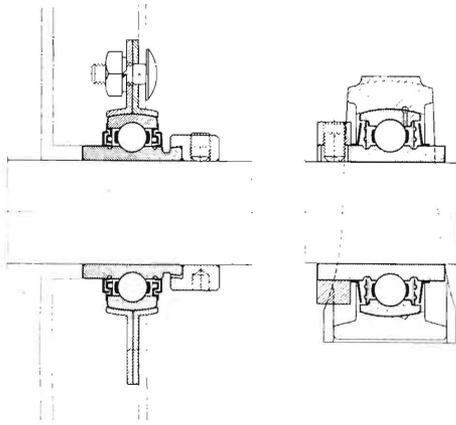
Abgedichtete einstellbare Rillenkugellager.
